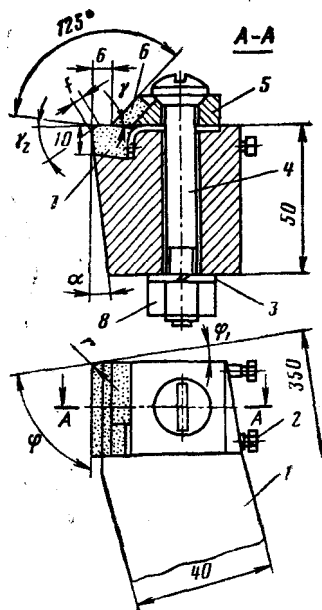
Проходной твердосплавный резец со стружколомающим устройством для предварительной обточки изношенных восстанавливаемых бандажей колесных пар: 1 — державка; 2 — регулировочный винт; 3 — шайба; 4 — болт; 5 — планка; 6 — стружколомающая пластина; 7 — режущая пластина; 8 — гайка
